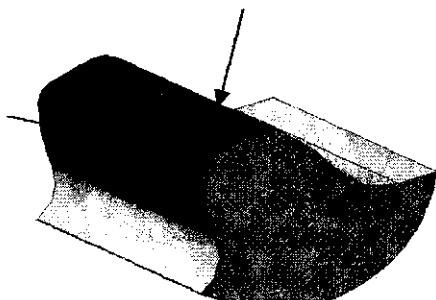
Обрабатываемая поверхность зуба (стрелками показаны скругленные продольные кромки зуба)
